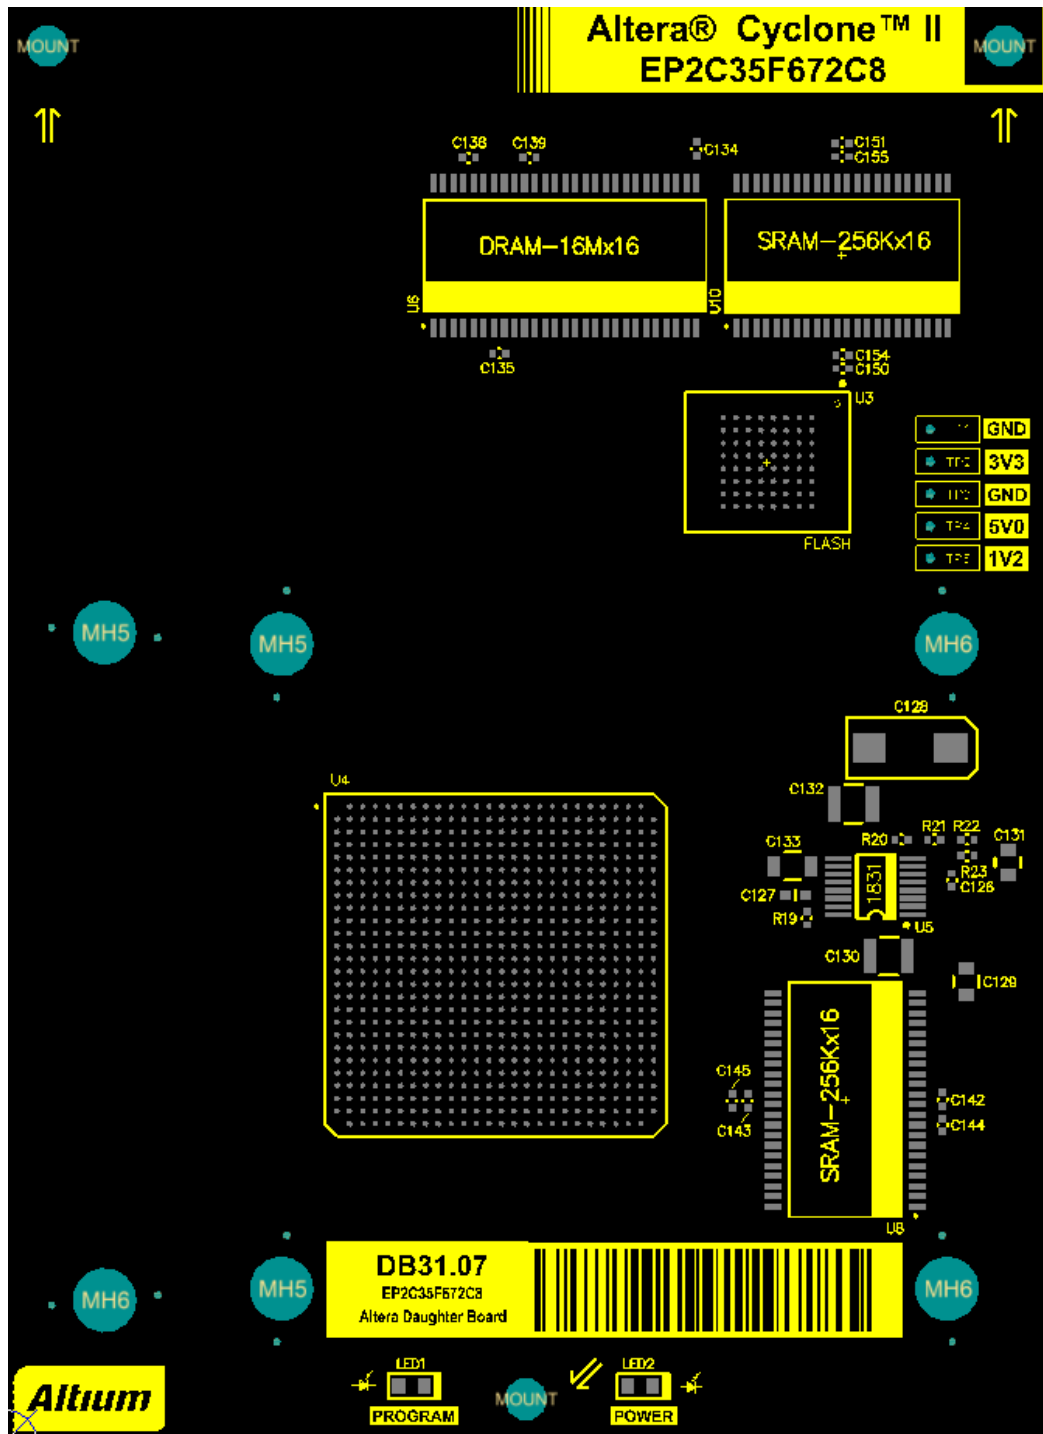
Ukázková DPS Developer tool DT01 v Altium Designer.
